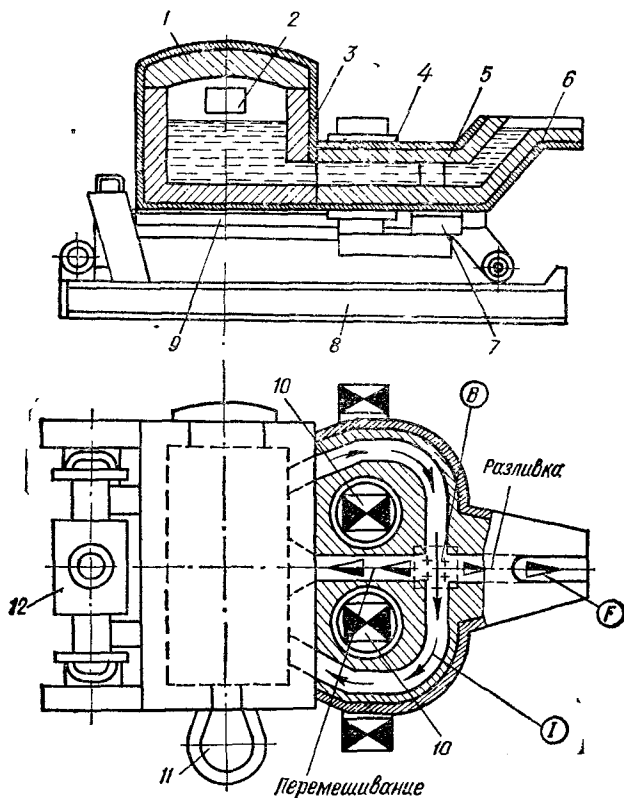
Схема магнитодинамической установки для чугуна:
